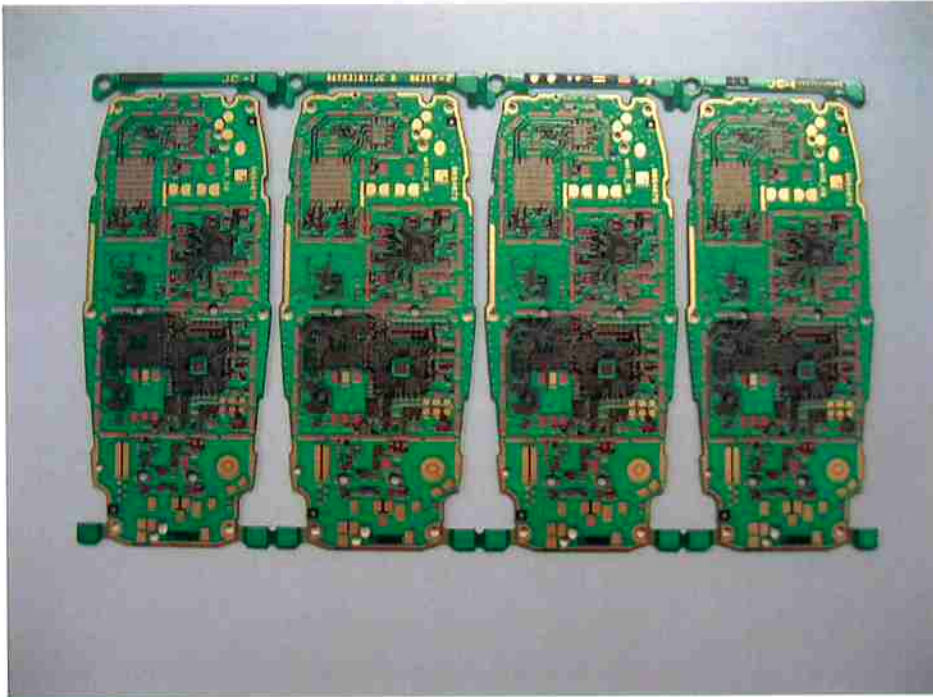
Conjunto de 4 Placas de Circuito Impresso a Serem Montadas na
